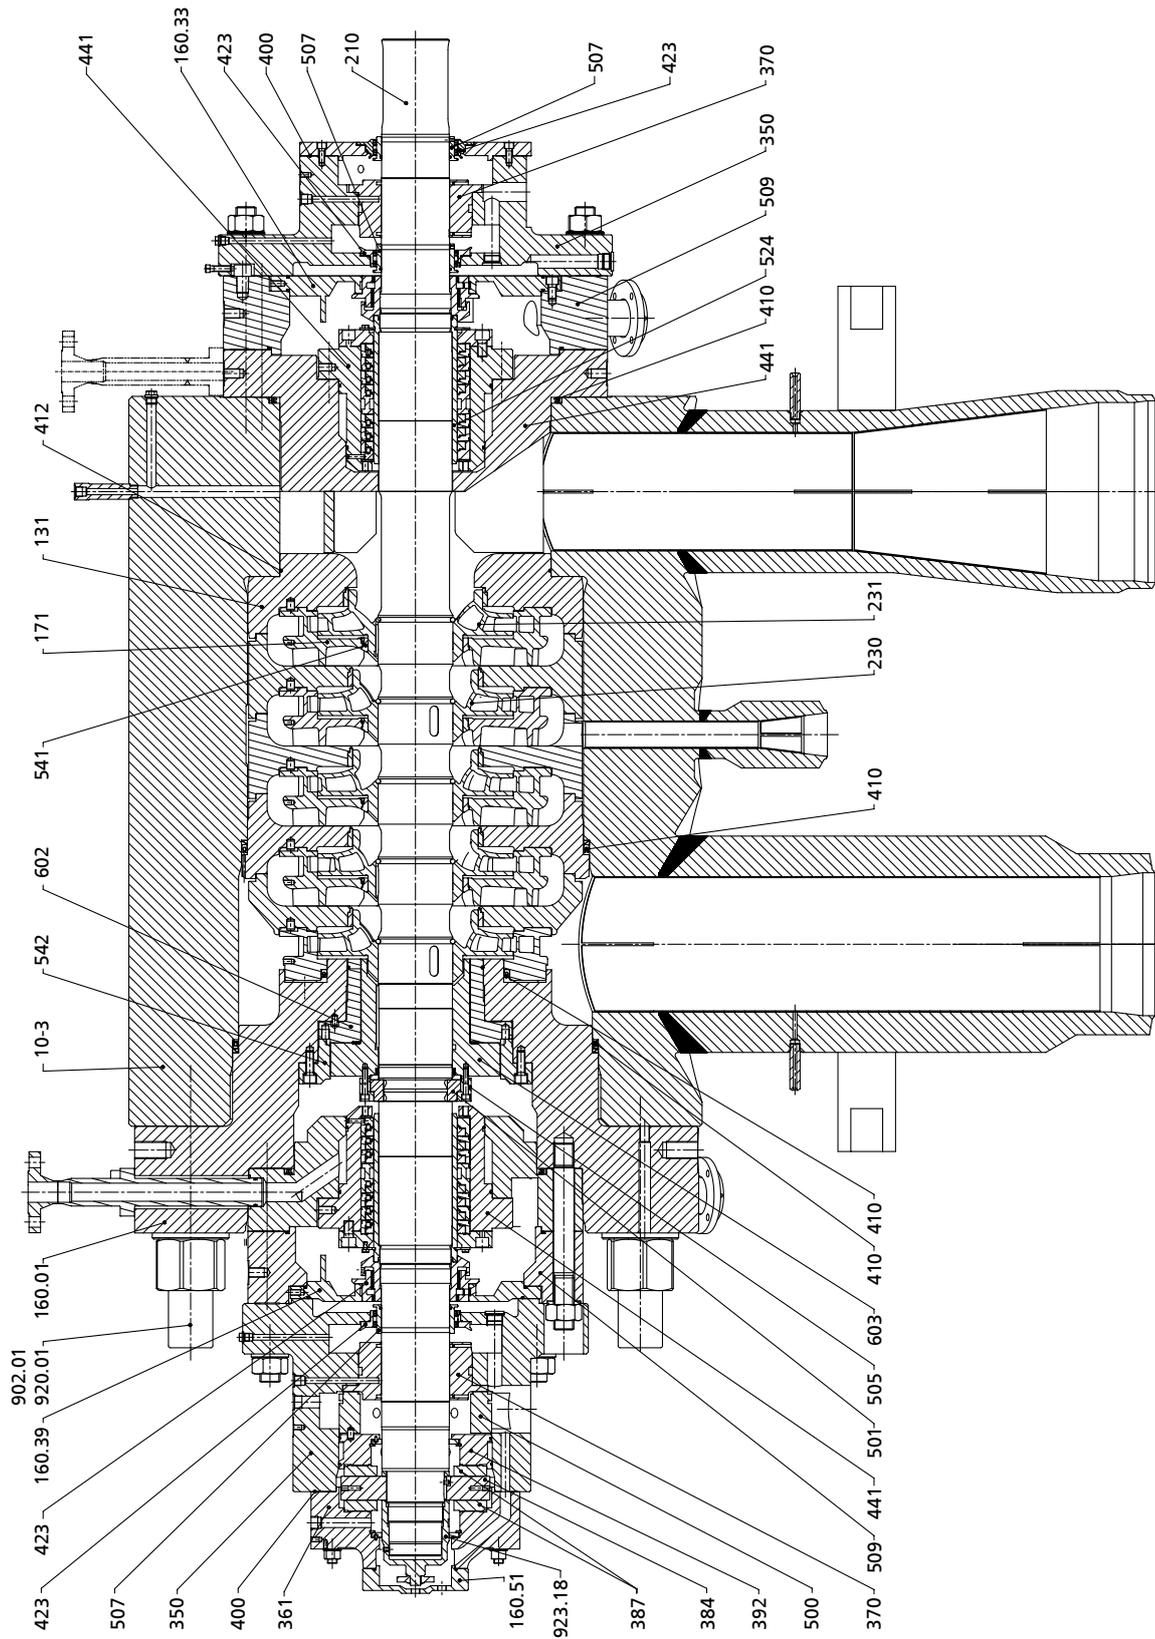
Gesamtzeichnung mit Einzelteilverzeichnis
